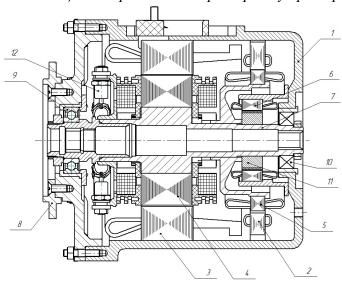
Основные узлы генератора: 1 — корпус; 2 — статор возбудителя; 3 — статор основного генератора; 4 — ротор основного генератора; 5 — ротор возбудителя; 6 — статор подвозбудителя; 7 — вал; 8 — щит; 9 — передний подшипник; 10 — задний подшипник; 11 — ротор подвозбудителя; 12 — вращающийся выпрямитель
